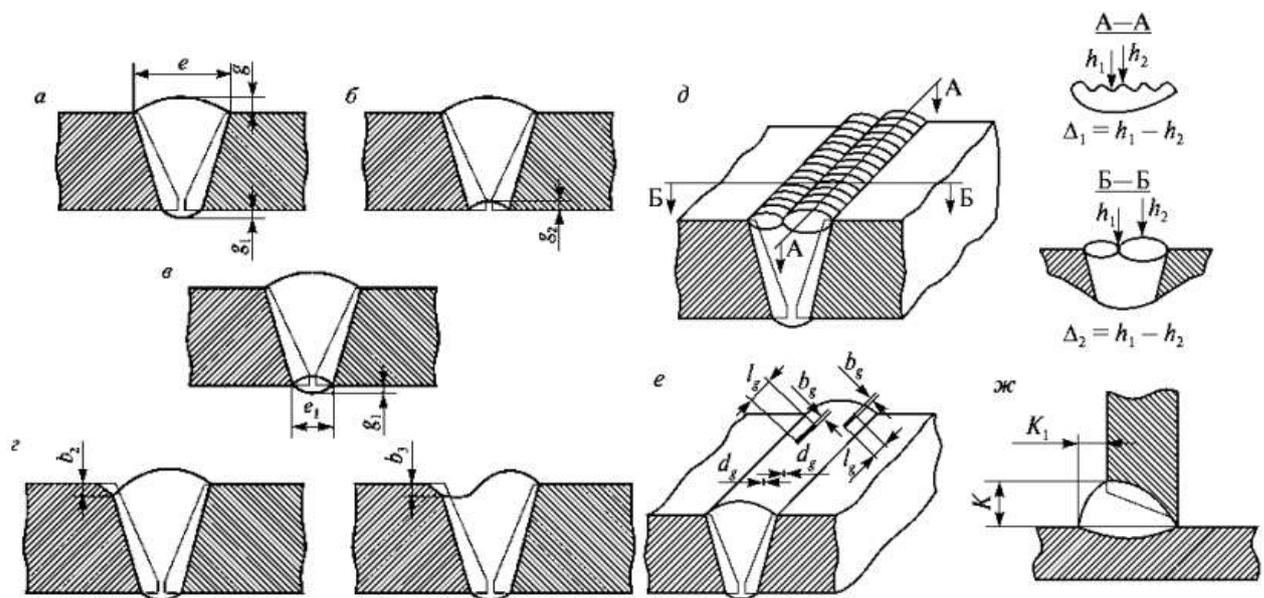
Конструктивные элементы и дефекты сварного шва, подлежащие измерительному контролю
